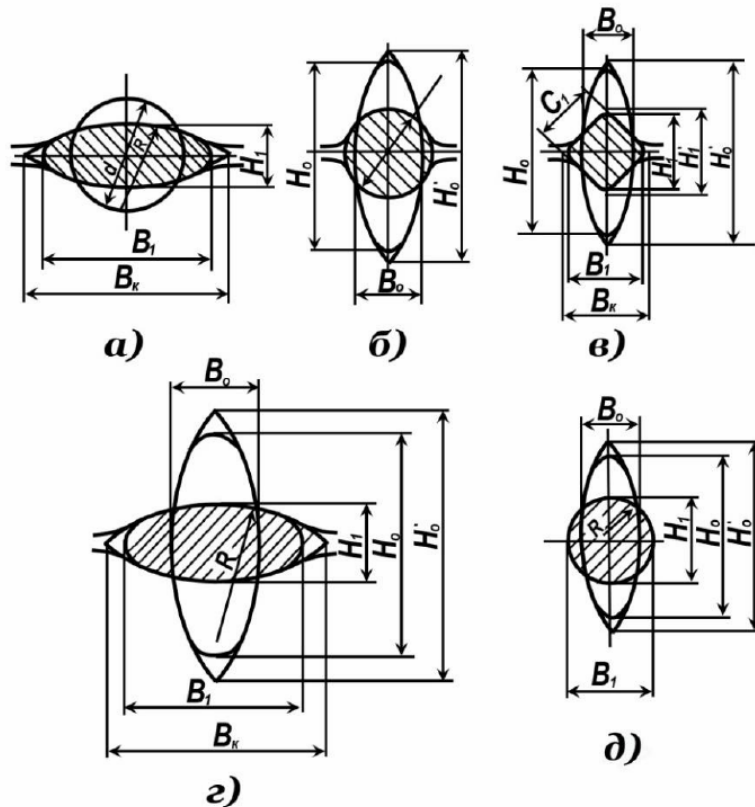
Схеми фасонування і геометричні елементи заготовок: а) – круг-овал; б) – овал-круг; в) – овал-квадрат; г) – овал-овал; д) – овал-ребровий овал
